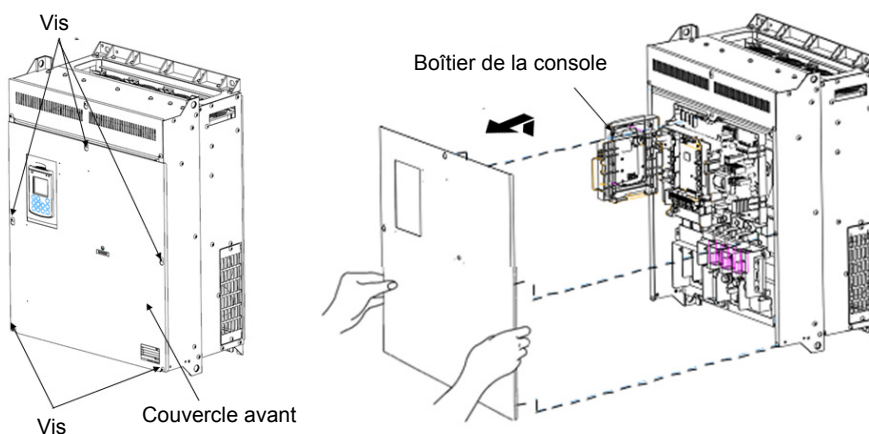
Retrait du couvercle avant et de la plaque de câblage (FRN110AQ1S-4□)
